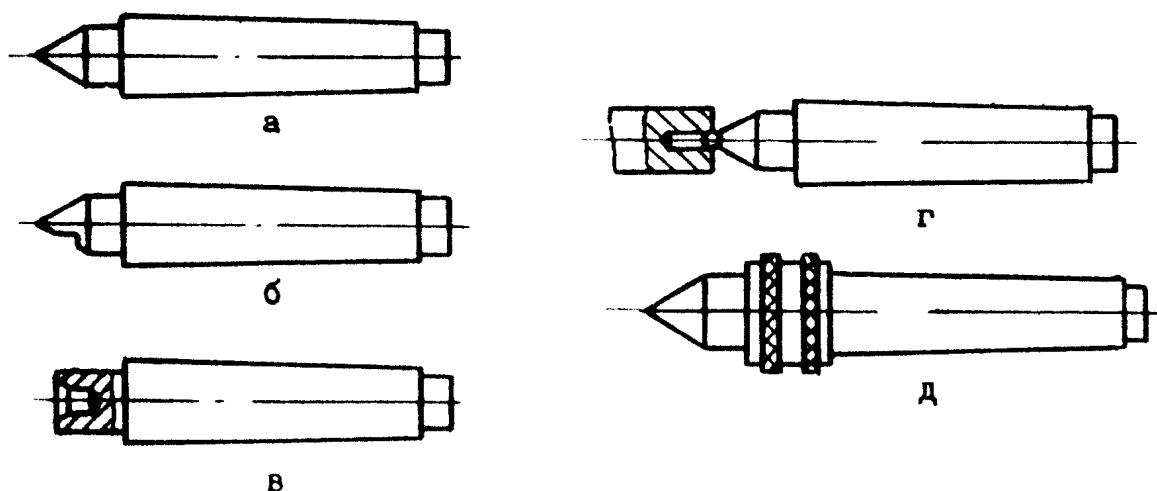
Центры токарных станков: а – опорный; б – срезанный; в – обратный; г – шариковый; д – вращающийся
